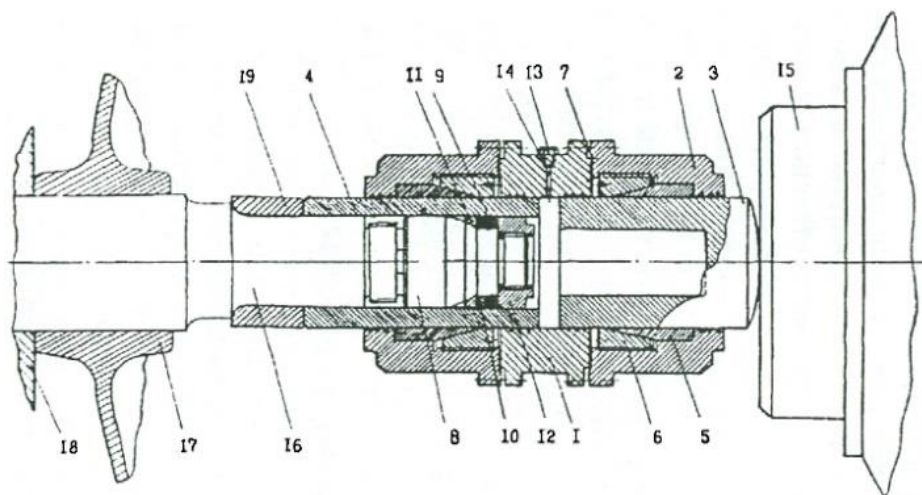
Устройство для распределения сдвигающего аксиального усилия на ось колёсной пары при механической распрессовке
